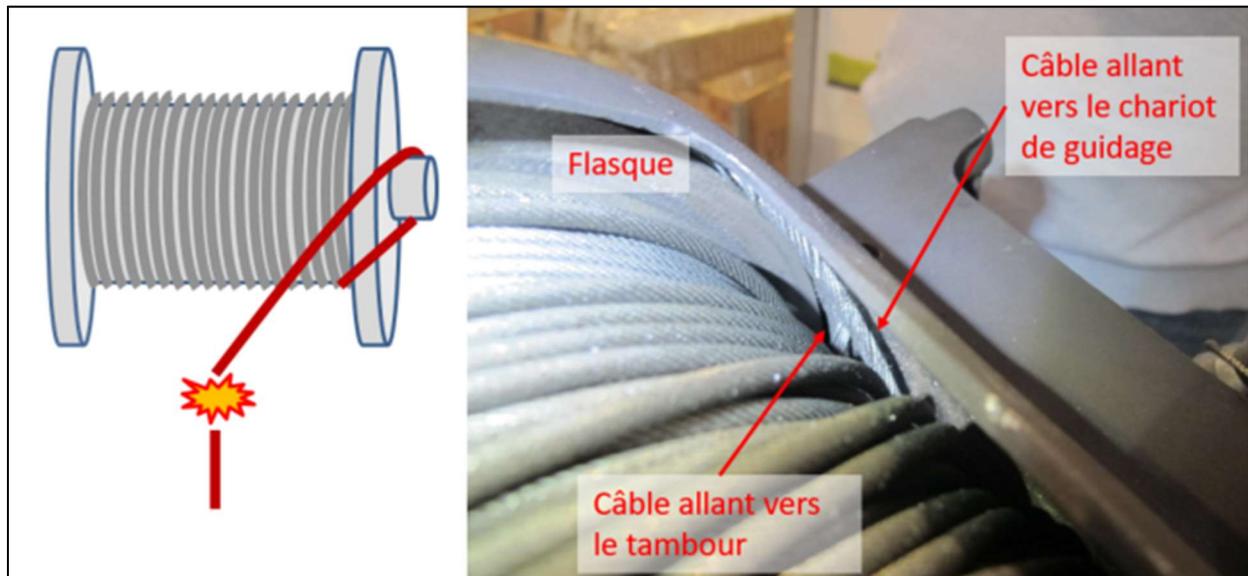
vue schématique et photo de la spire passée derrière le flasque
